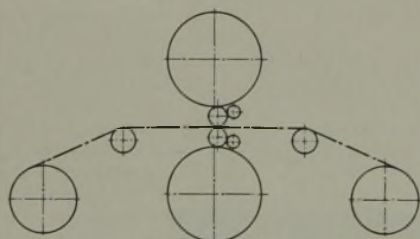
Umkehrwalzwerk mit je einer Ziehwickeltrommel vor und hinter dem Gerüst.
